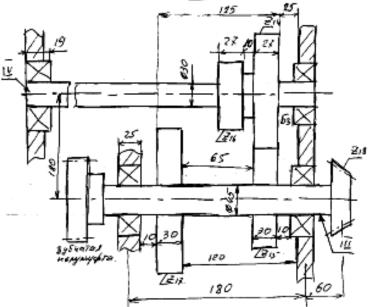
Компоновочная схема развертки наиболее нагруженной группы передач
